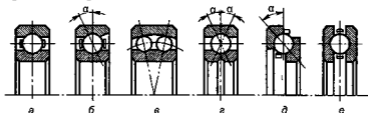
Шариковые подшипники качения: а – радиальный; б – радиально-упорный; в – радиальный двухрядный сферический; г – радиально-упорный однорядный четырехточечный; д – упорно-радиальный; е – упорный
